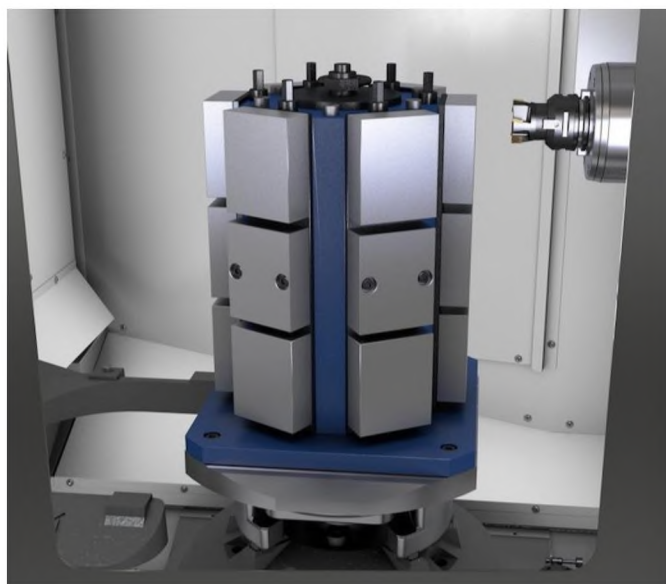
Робочі органи верстата Haas EC-400
